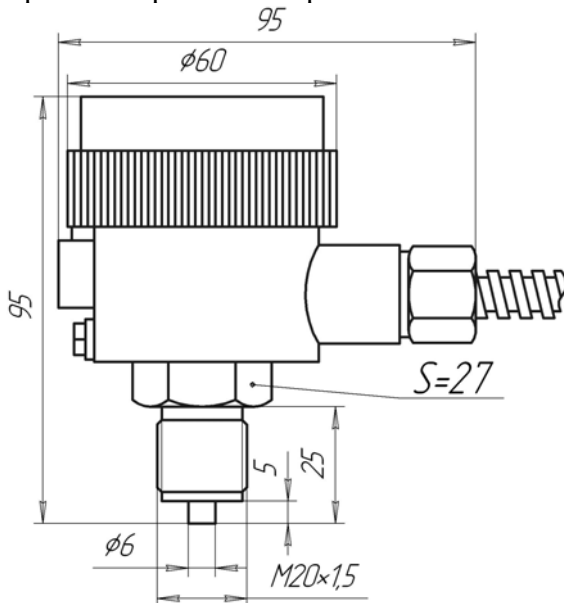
Модель 1190. Взрывозащита, нержавеющий корпус, встроенный кабель.
